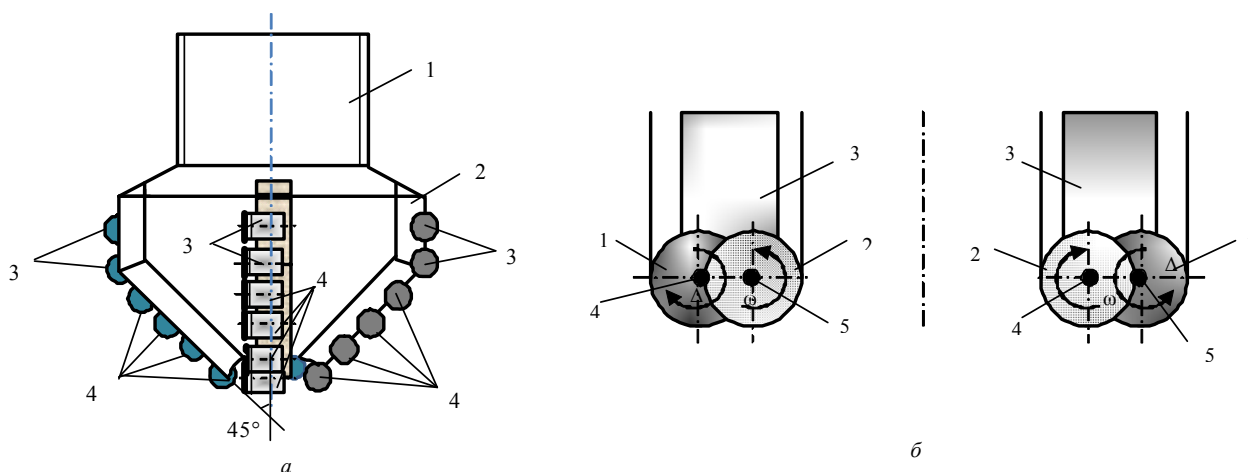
Буровые инструменты с вращающимися резцами PDC: *a* – долото, где 1 – корпус с резьбой; 2 – матрица; 3 и 4 – вращающиеся резцы; *б* – коронка, где 1 – скважинообразующий вращающийся резец; 2 – кернаобразующий резец; 3 – корпус; 4 и 5 – оси вращения резцов
